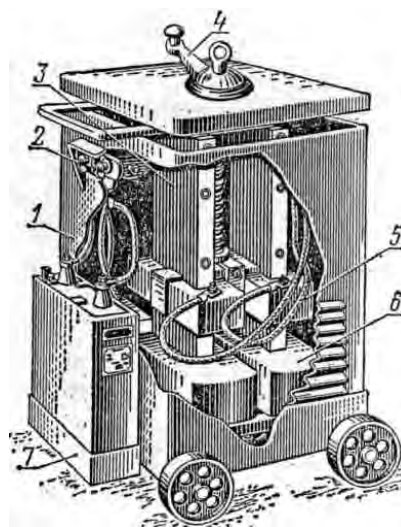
Сварочный трансформатор ТСК-500:
